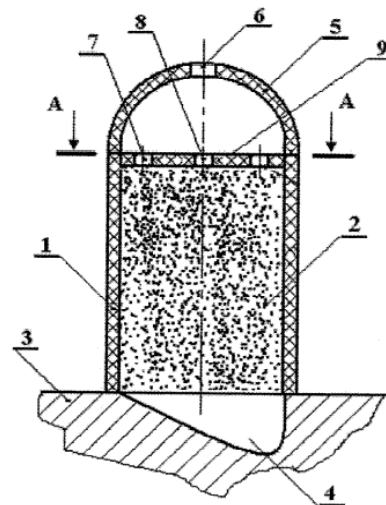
Устройство для ремонта деталей с открытыми поверхностными дефектами
